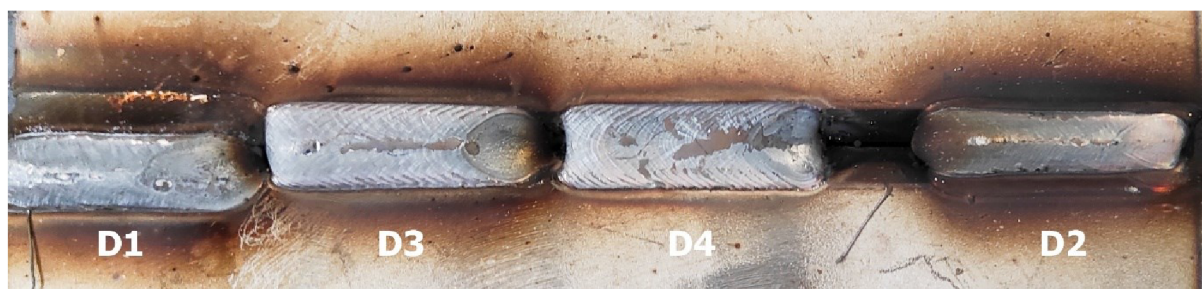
VZORKY C - KOREŇOVA VRSTVA ZVARU
